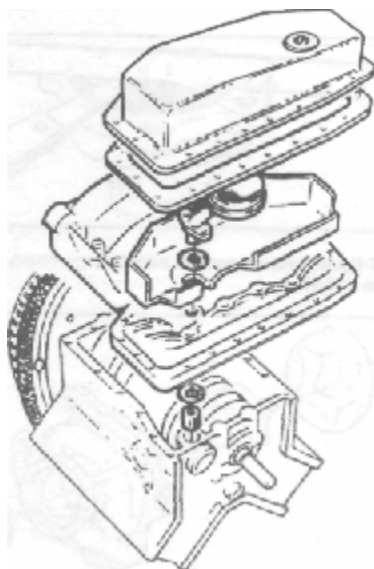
Снятие масляного поддона и нижних деталей картера — Двигатель B280F
